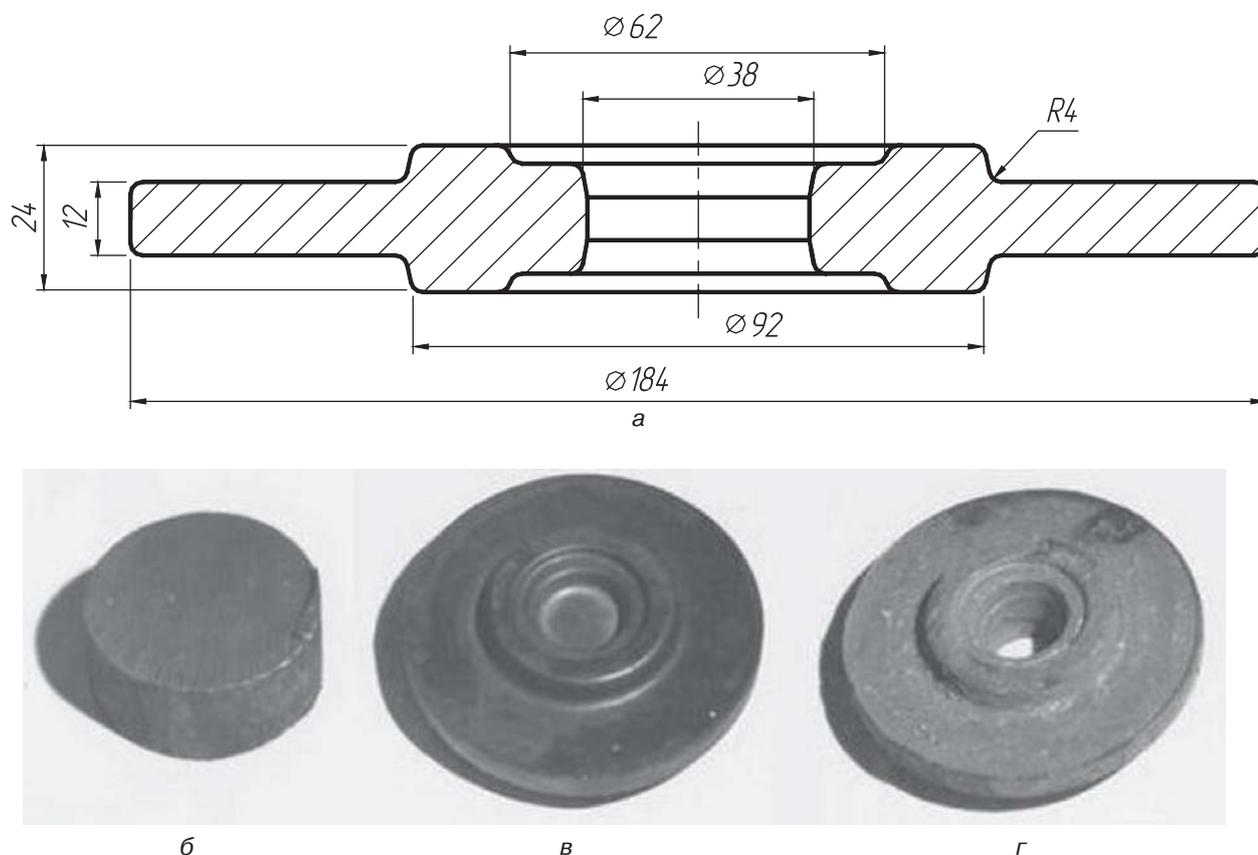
Поковка «каретка синхронизатора» автомобиля ЗиЛ 4331:
